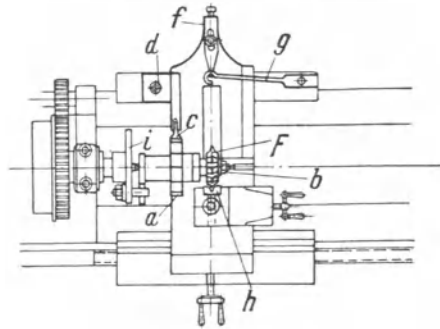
Hinderdrehvorrichtung für Fräser (umgebaute Drehbank).
